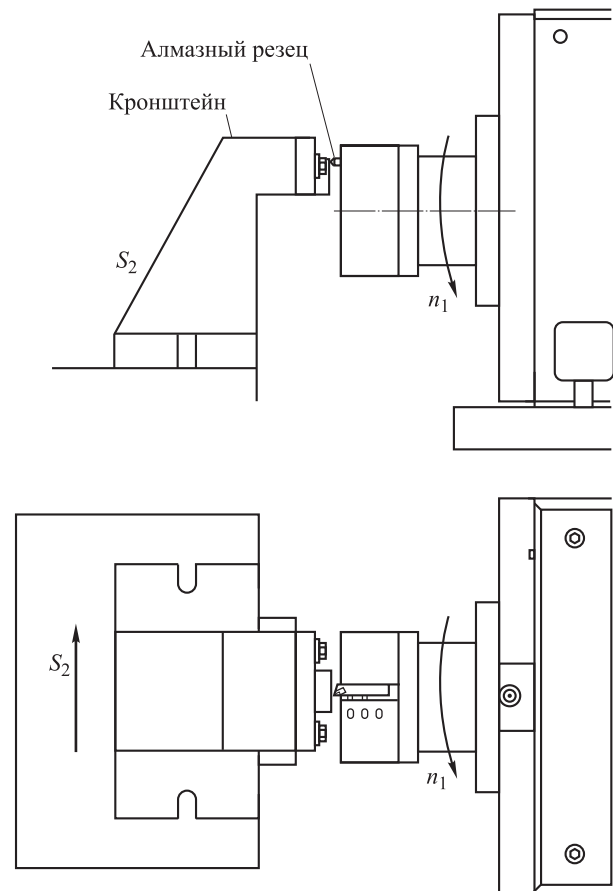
Кинематическая схема обработки поверхности заготовки однорезцовой алмазной фрезерной головкой
